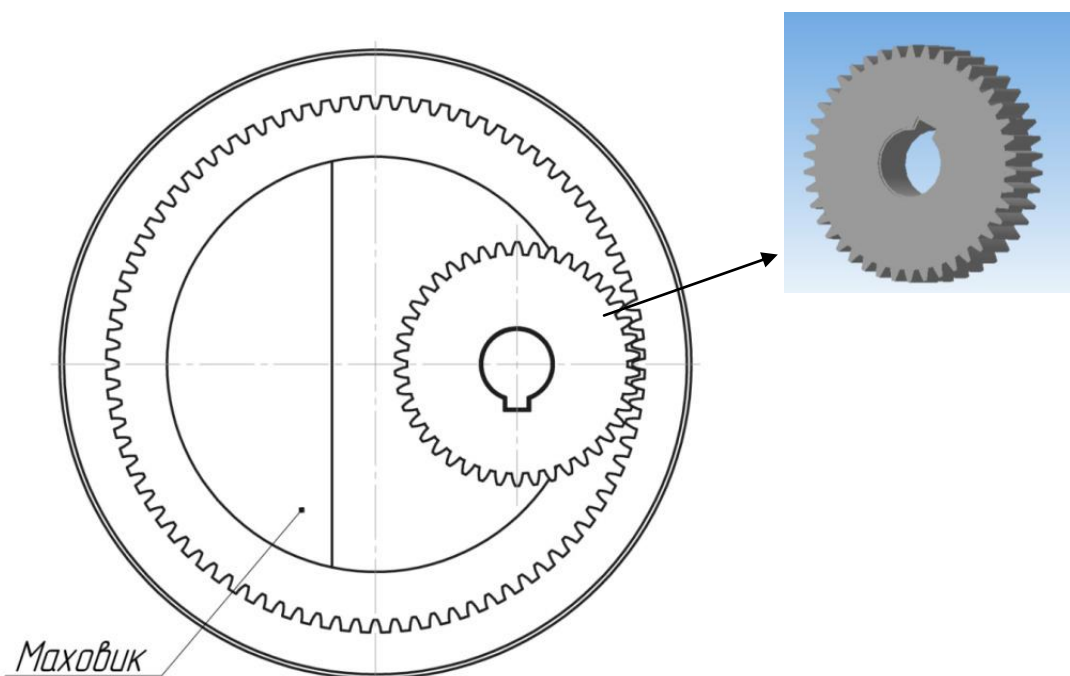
Механізм передачі руху від шпинделя верстата до зубчастого колеса.
